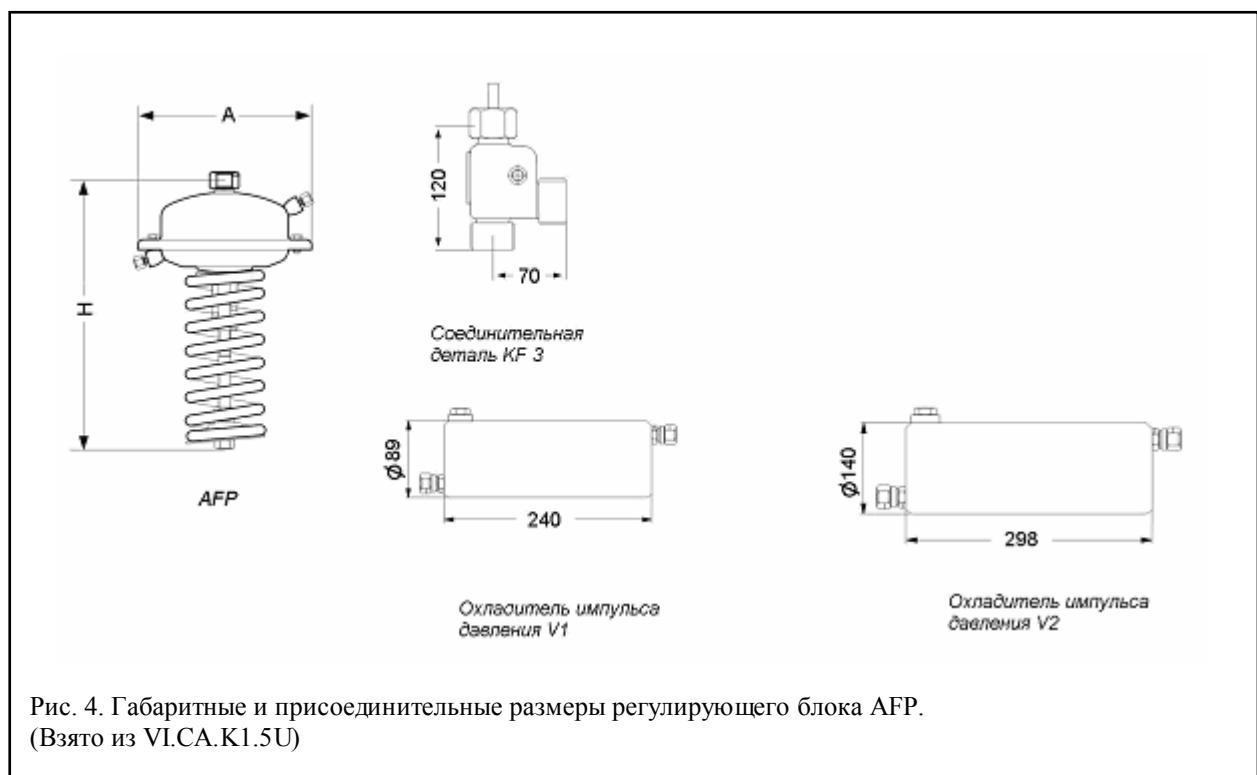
Габаритные и присоединительные размеры регулирующего блока AFP.
